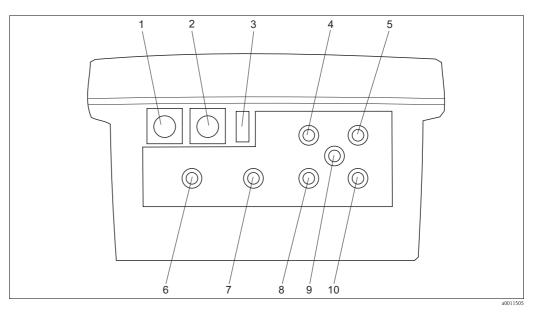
Anschlüsse des Messumformers (Aluminiumausführung)
